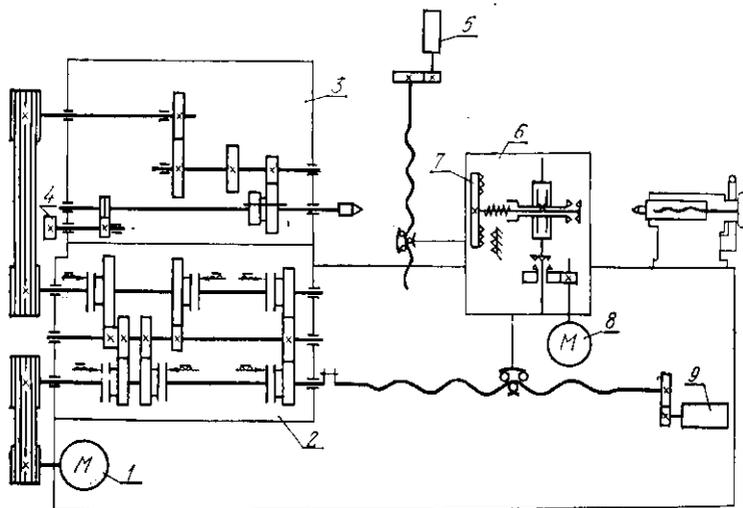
Кинематическая схема токарного станка с ЧПУ модели 16K20ФЗС4
